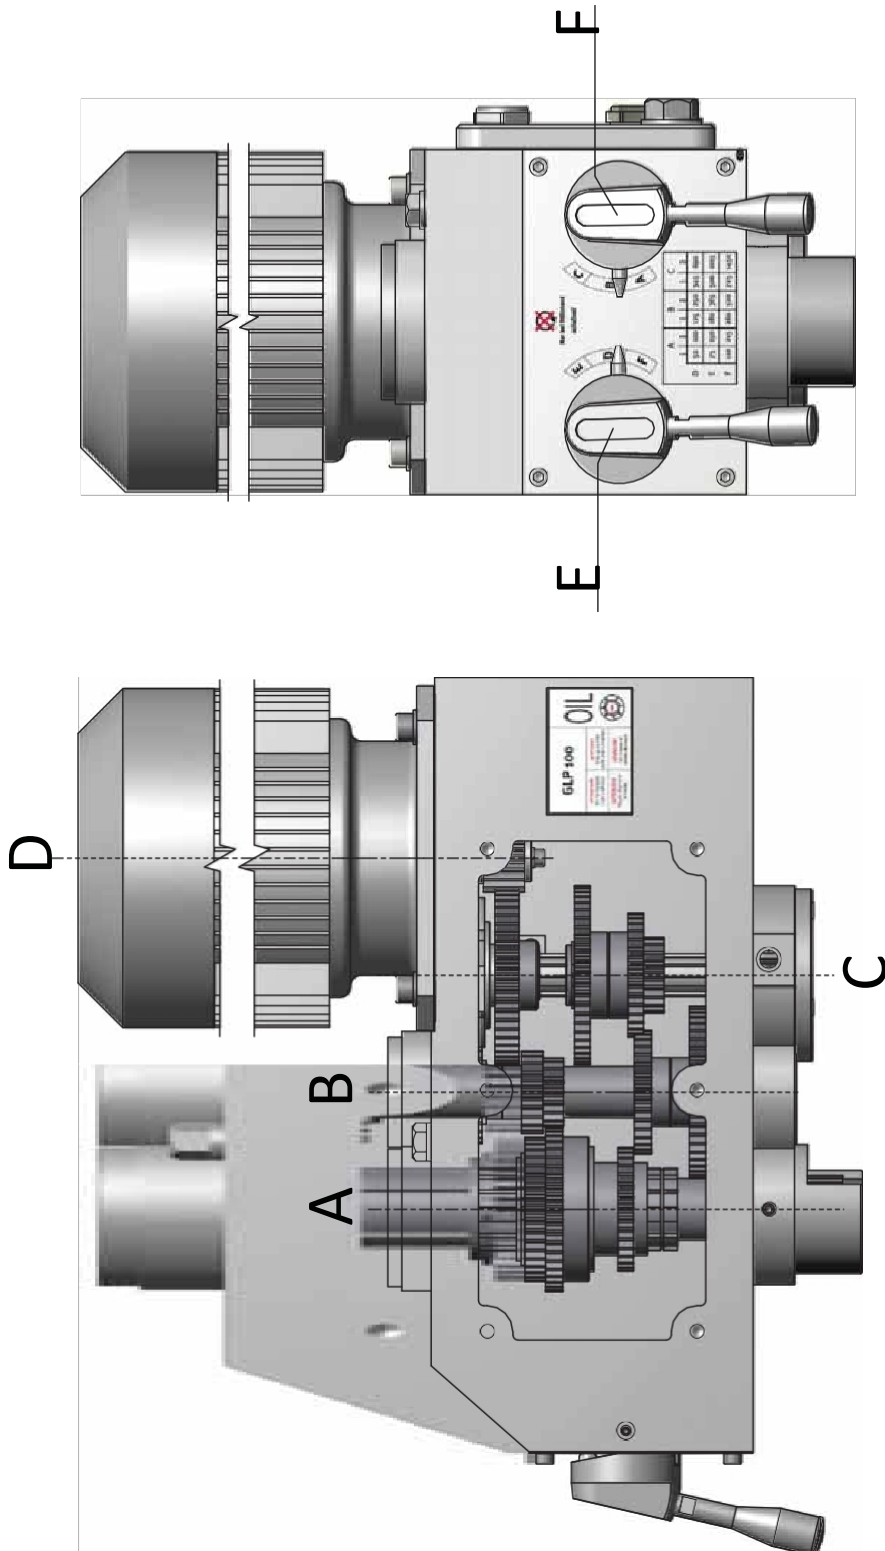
Getriebe Bohrspindel - Broche principale de la boîte de vitesses
